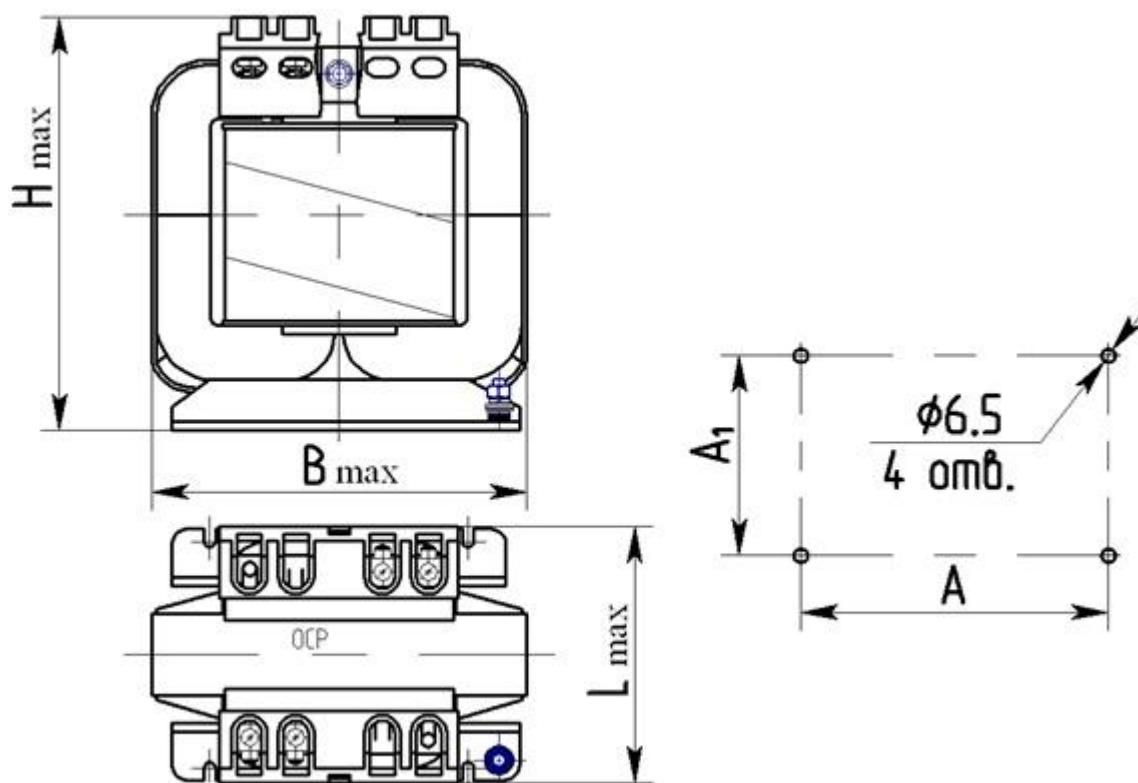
Габаритные размеры трансформаторов и расположение отверстий для установки
